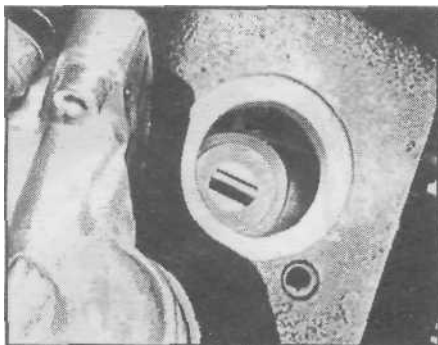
, б. Снятие кольца крепления пластины подшипника
